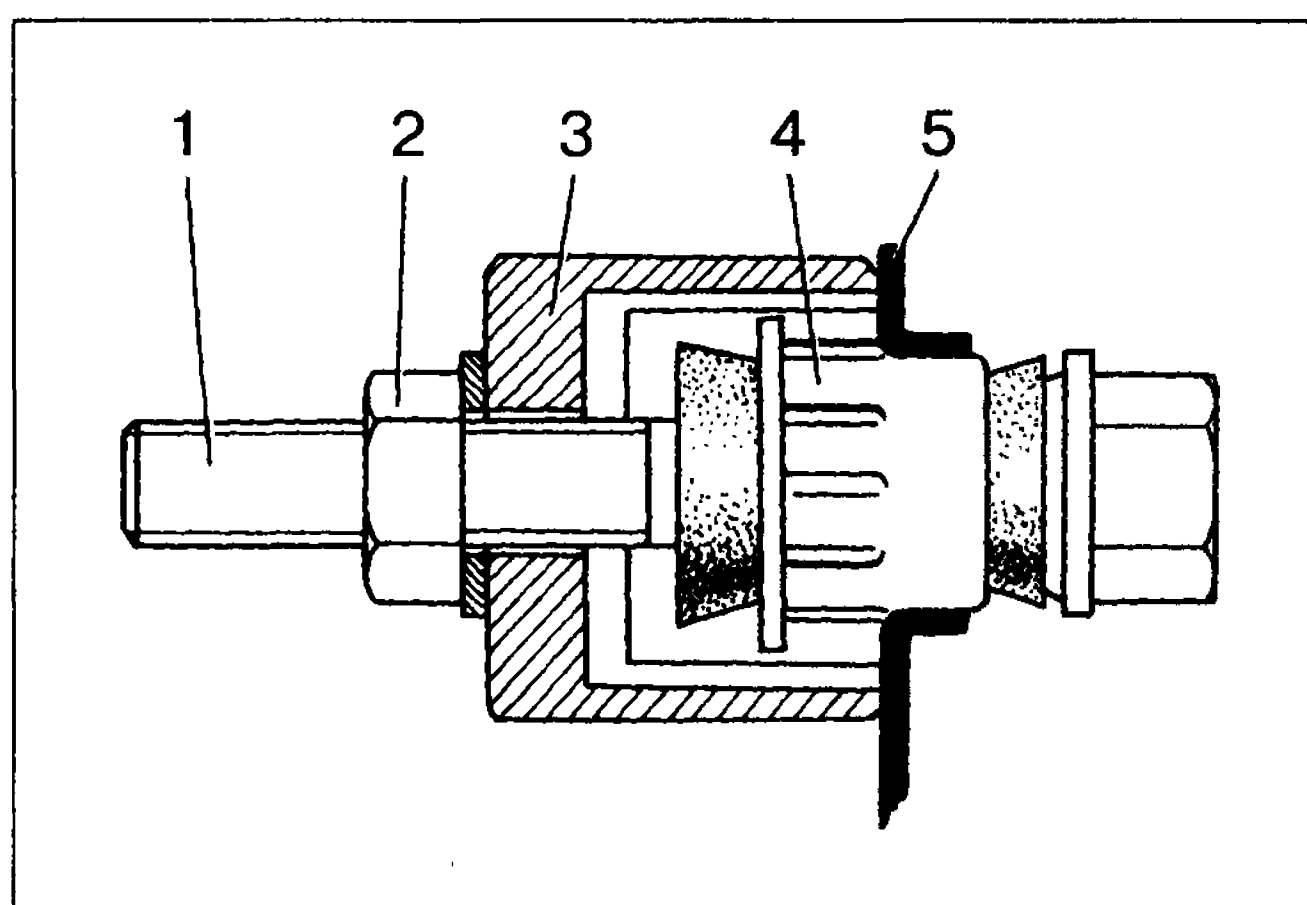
Схема выпрессовки шарнира верхнего рычага: 1-болт; 2-гайка; 3-стакан приспособления А.47046; 4-шарнир; 5-верхний рычаг
